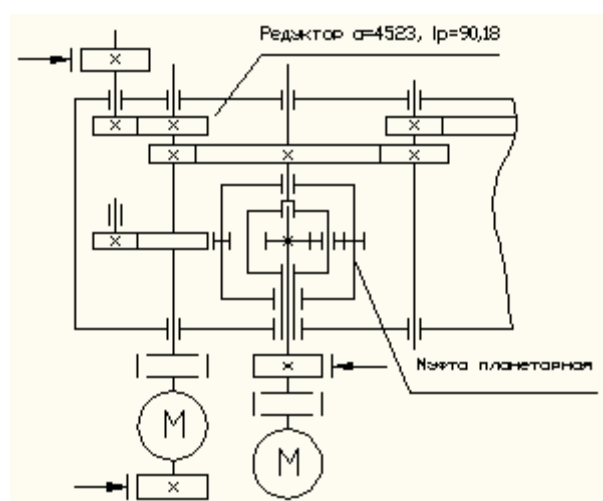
Редуктор механизма подъема с встроенной планетарной муфтой
